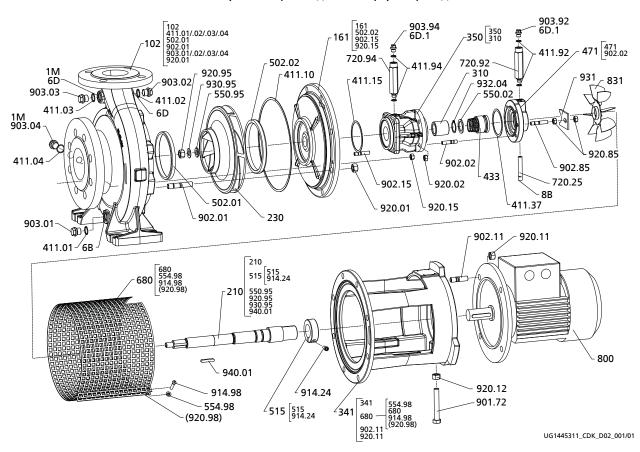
Чертеж общего вида со спецификацией деталей Etabloc SYT
